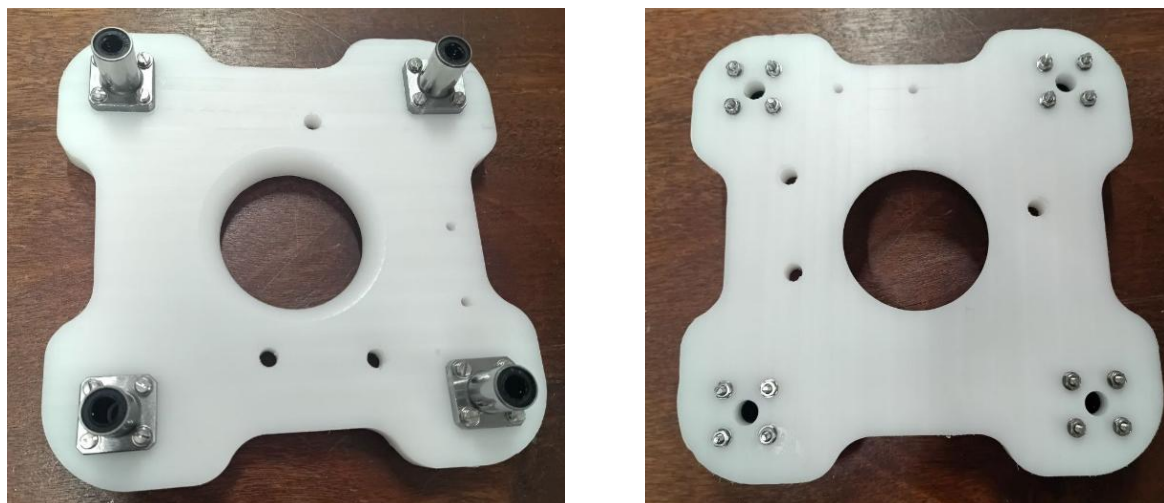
Внешний вид нижней подвижной пластины с линейными подшипниками
